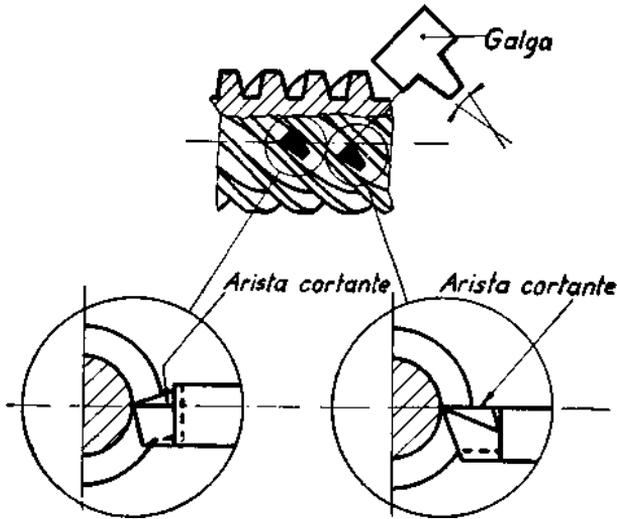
Acabado por separado de los flancos con la arista cortante en el plano horizontal y centrada
